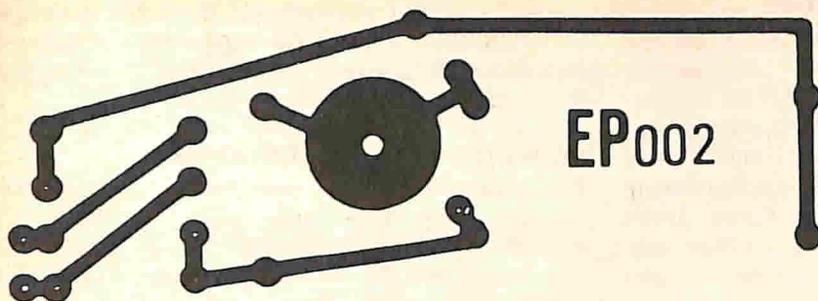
Disegno del circuito stampato necessario per il montaggio del filtro dell'alimentatore.
